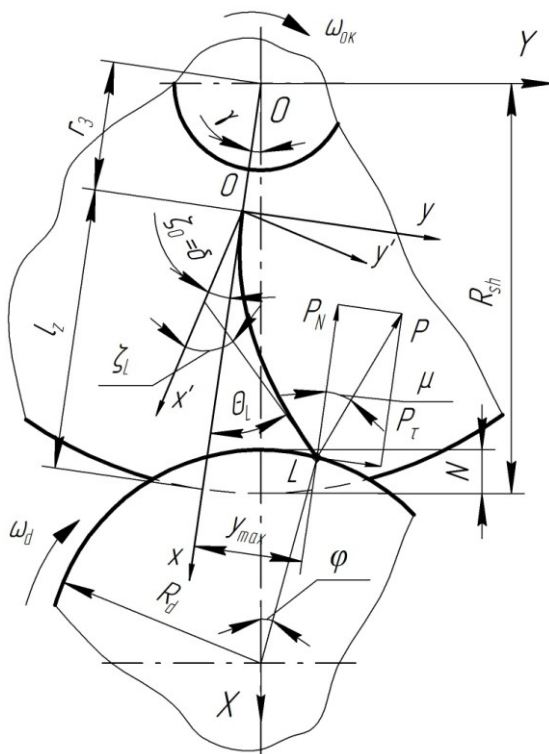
Схема контакта ворса с обрабатываемой поверхностью
